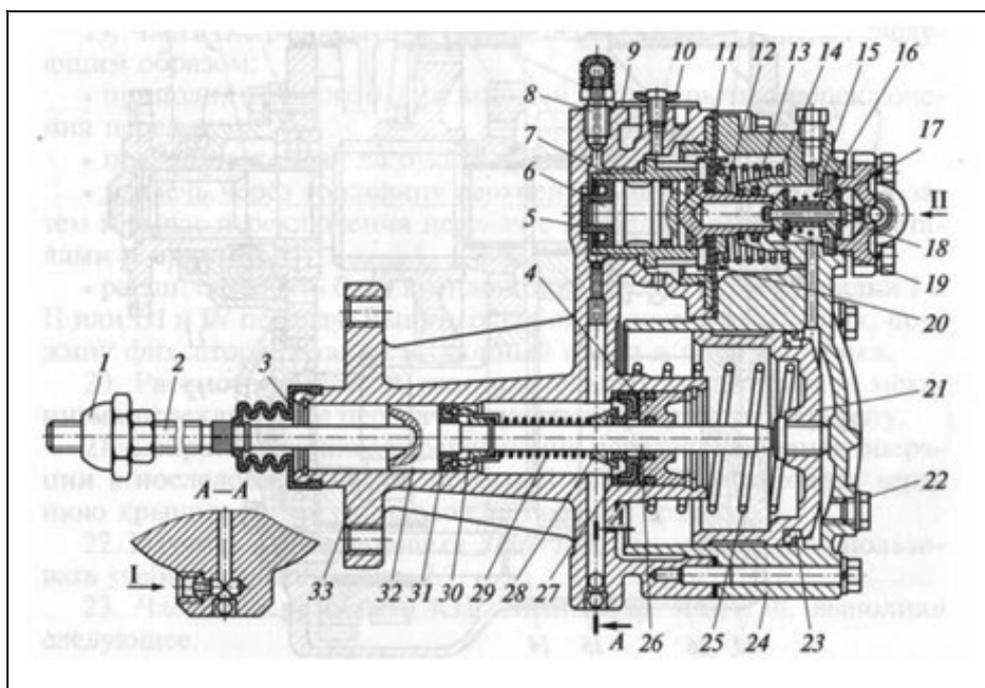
Сцепление в автомобилях семейства КамАЗ:
